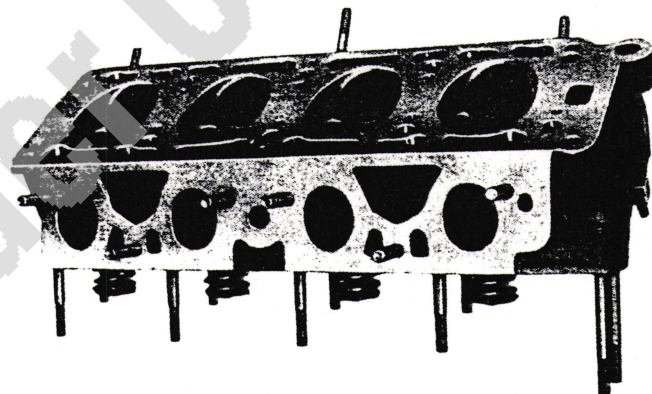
Ansicht des Zylinderkopfes von unten.
